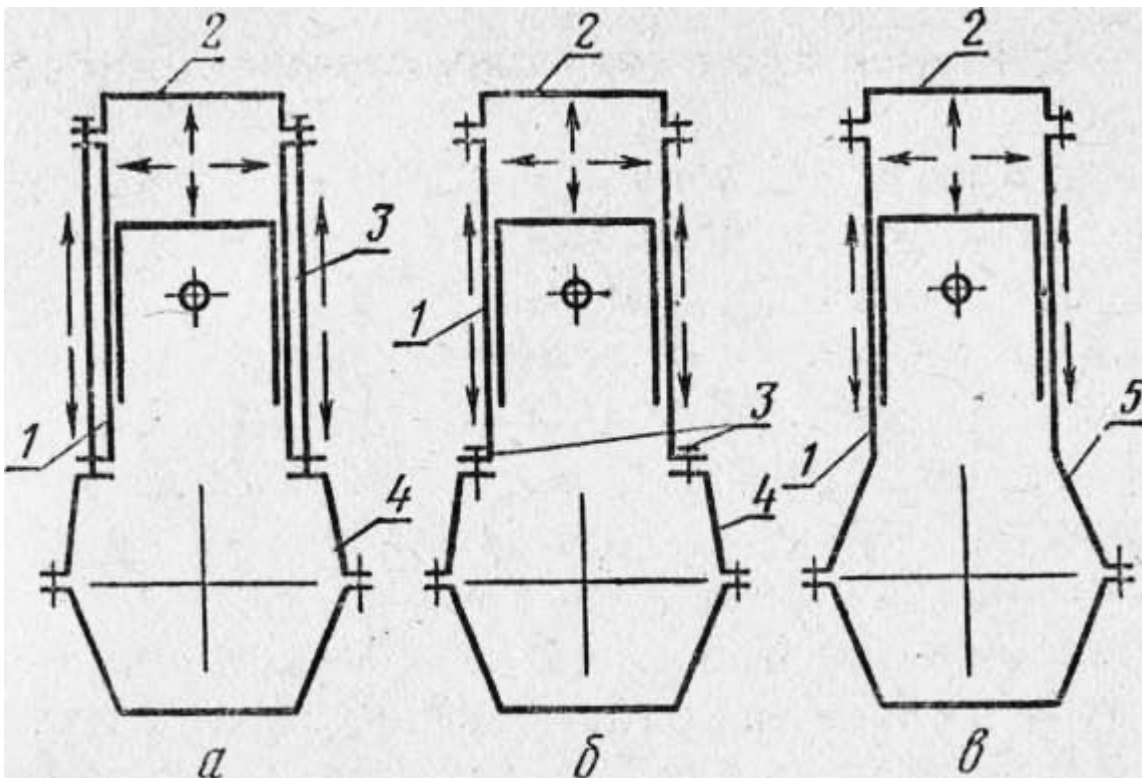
Конструктивные схемы цилиндров двигателей: а — отдельно изготовленный цилиндр; б — блок цилиндров; в - цилиндры в блок-картере; 1 — цилиндр; 2 — головка цилиндра; 3 — детали крепления цилиндра к картеру; 4 — картер; б — блок-картер
